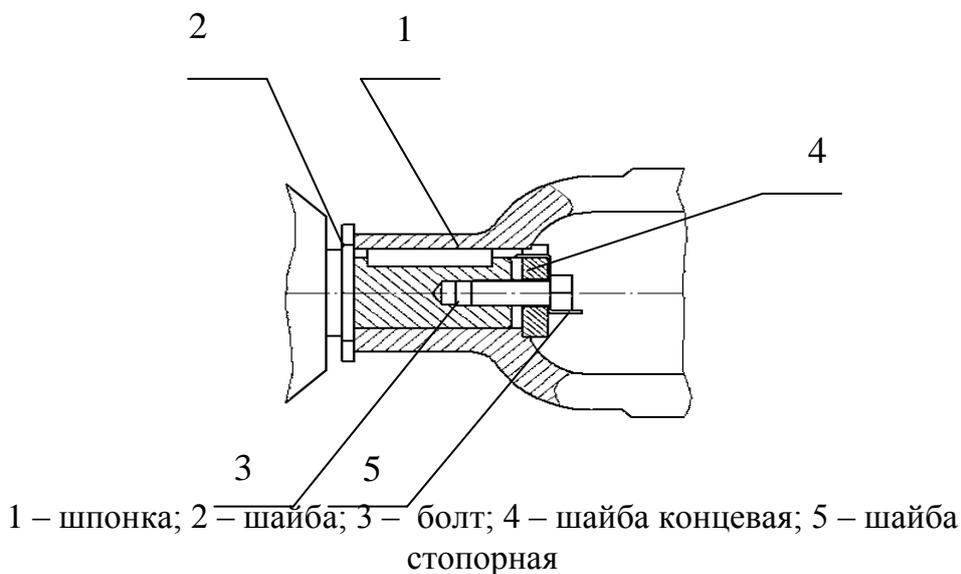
Крепление вилок шарниров карданных валов на валах редуктора
